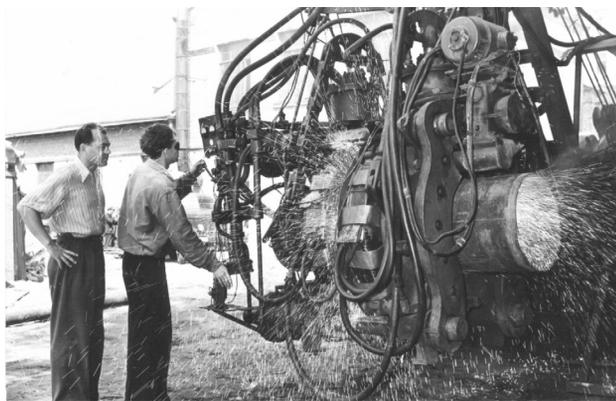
Эксперименты по контактной сварке непрерывным оплавлением, ИЭС им. Е.О. Патона, 1956 г.
